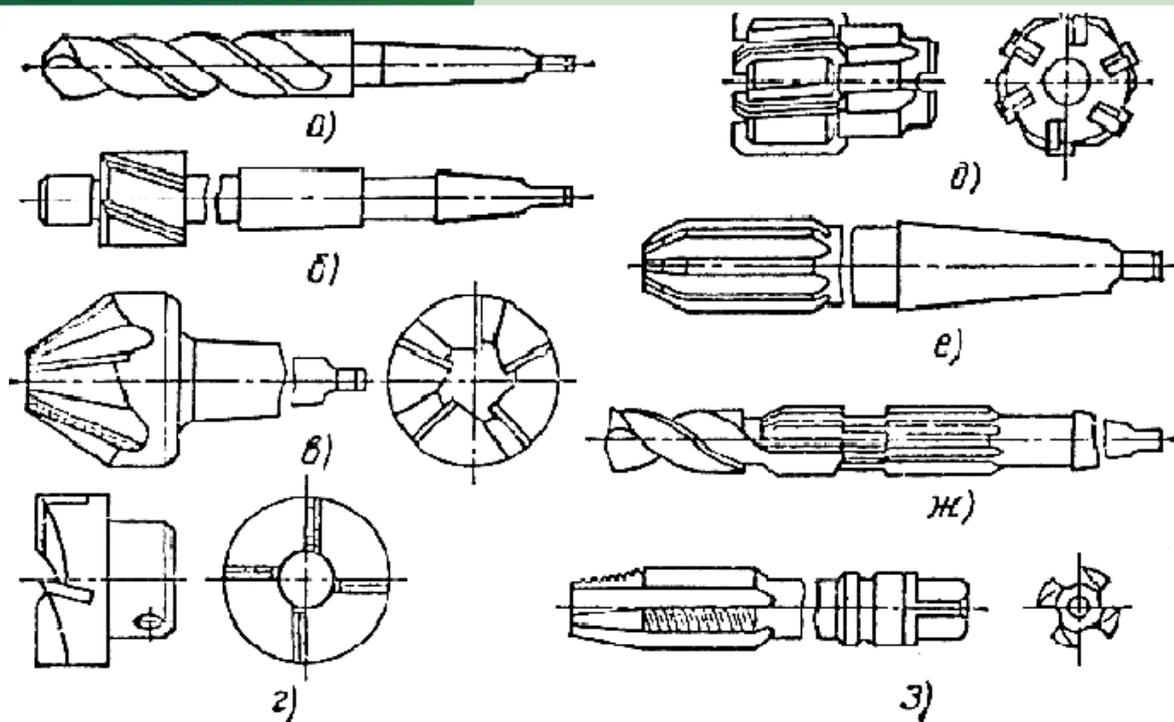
Режущие инструменты, применяемые на сверлильных станках
